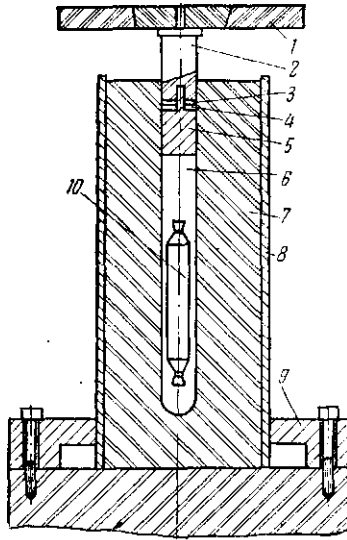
Установка для гидростатического прессования керамических и металлических порошков (Кошуба и Ставролакис):
